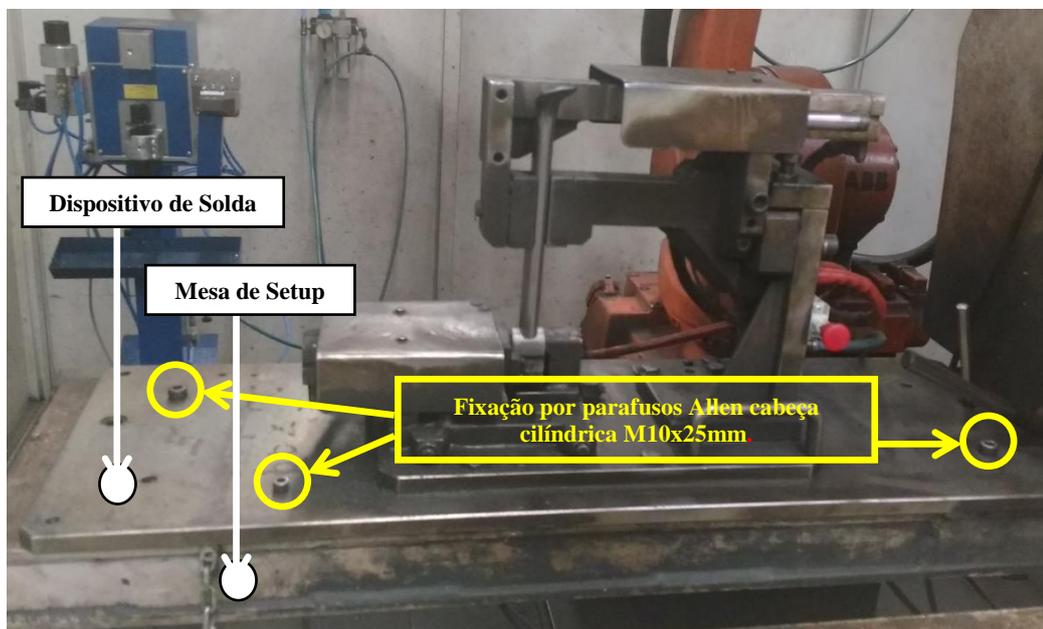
Dispositivo de solda fixado na mesa de setup por parafusos Allen cabeça cilíndrica M10x25mm.
